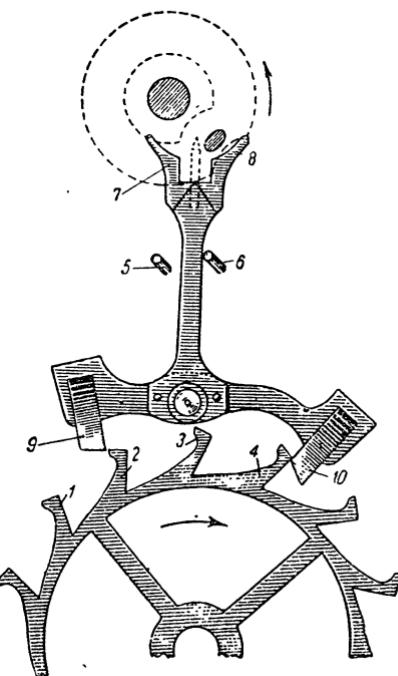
Анкерный спуск с неравноплечим якорем: 1, 2, 3 и 4—зубья анкерного колеса; 5—левый ограничительный штифт; 6—правый ограничительный штифт; 7—левый рожок вилки; 8—правый рожок вилки; 9—входная палета; 10—выходная палета
